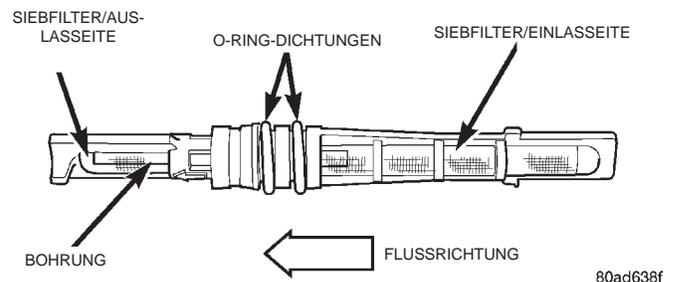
Rohr mit kalibrierter Bohrung—Typisch
